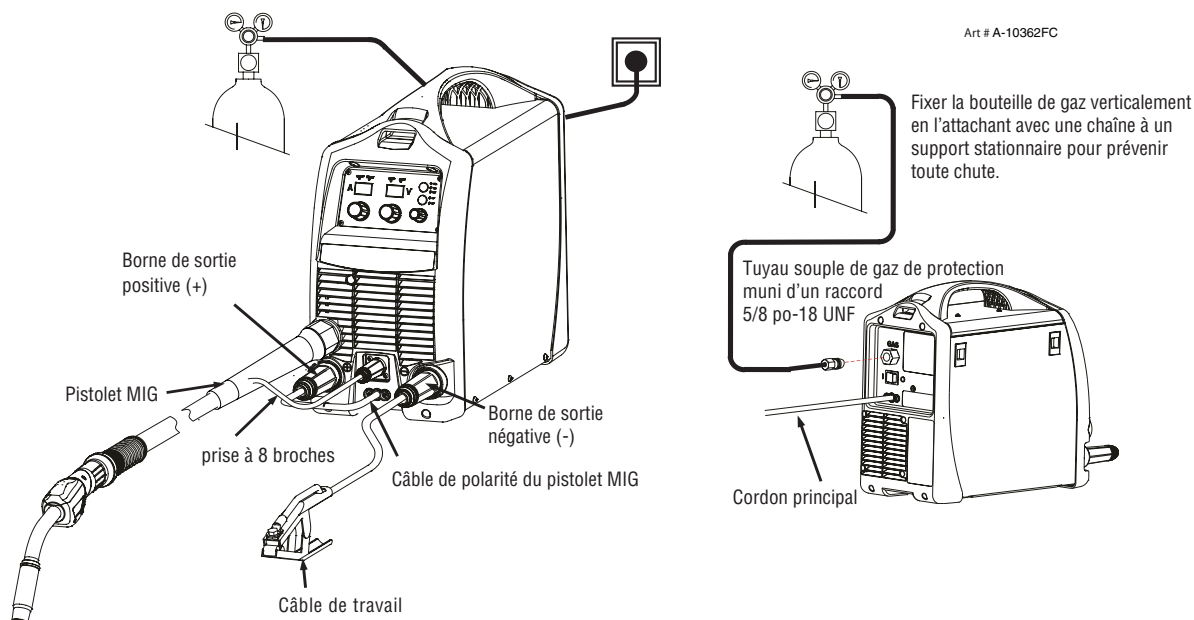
Configuration pour soudage MIG avec fil MIG sous protection gazeuse
